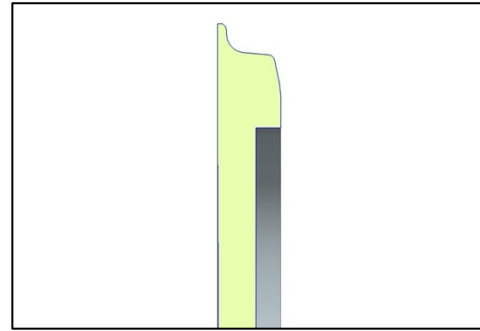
Gedrehte Werkzeugkontur [42]
